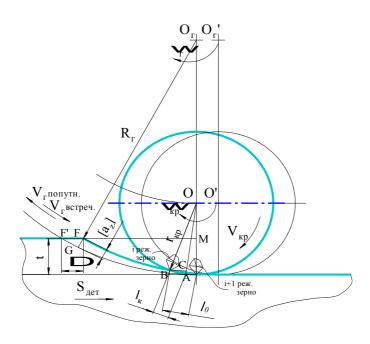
Условная схема расположения и взаимодействия режущих абразивных зерен с обрабатываемой поверхностью
